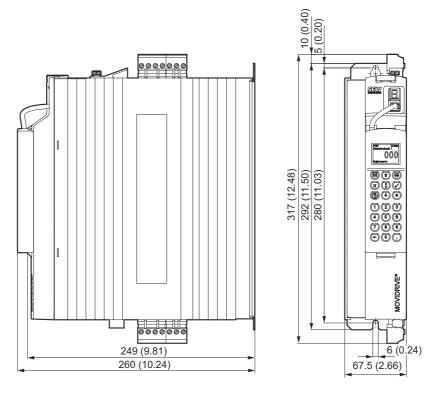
Dimensões MDX60B, tamanho 0M, dimensões em mm (in)
